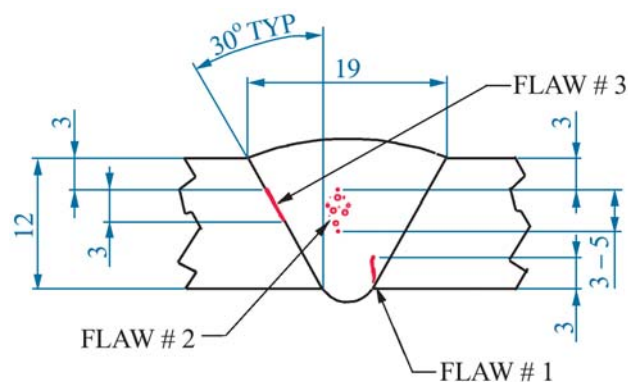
Поперечное сечение сварного шва с дефектами
